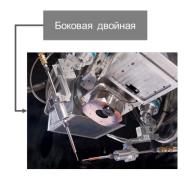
Центр сварочной техники и лазерной обработки Крэнфилдского университета, Великобритания
